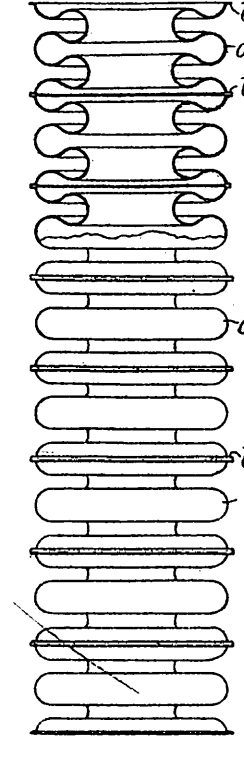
bis 32. Geschweißter Schlauch, schraubenförmig gewickelt.
